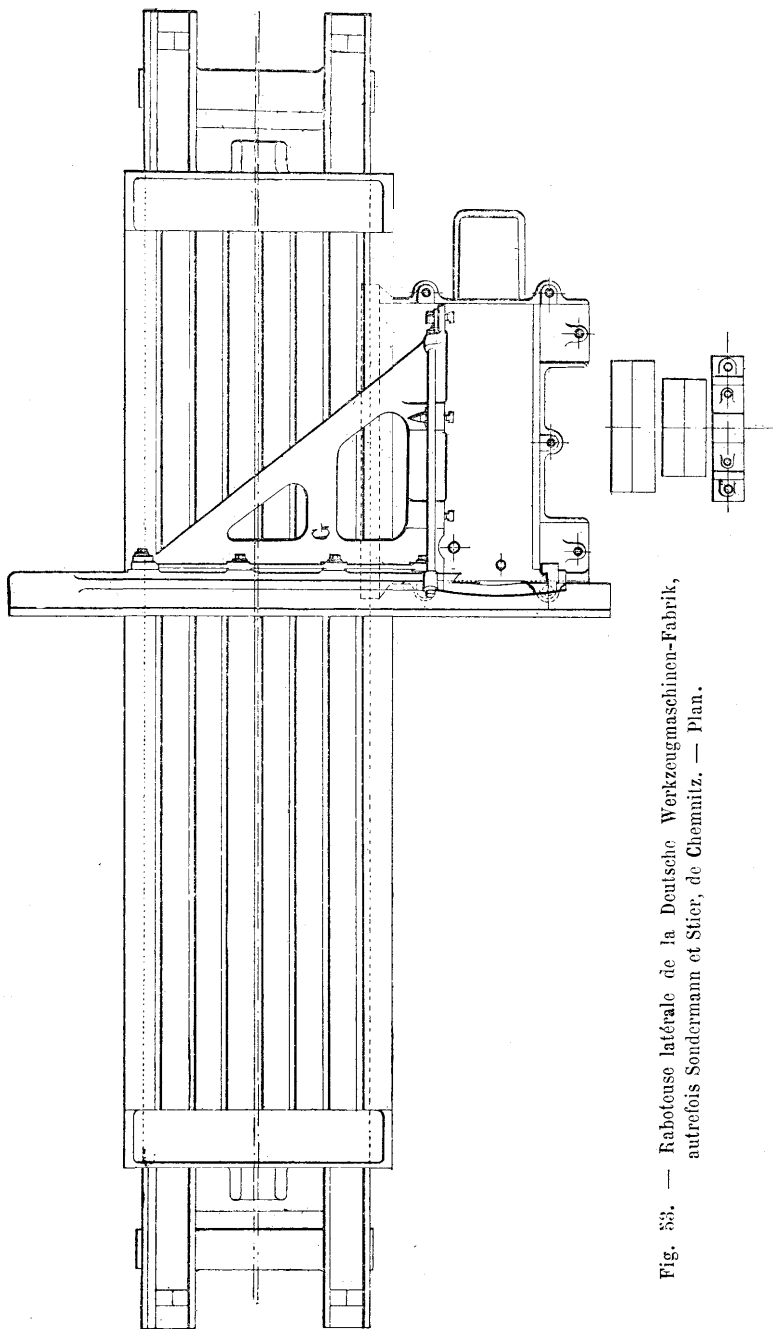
Rabotouse latérale de la Deutsche Werkzeugmaschinen-Fabrik, autrefois Sonderrmann et Stier, de Chemnitz. — Plan.
